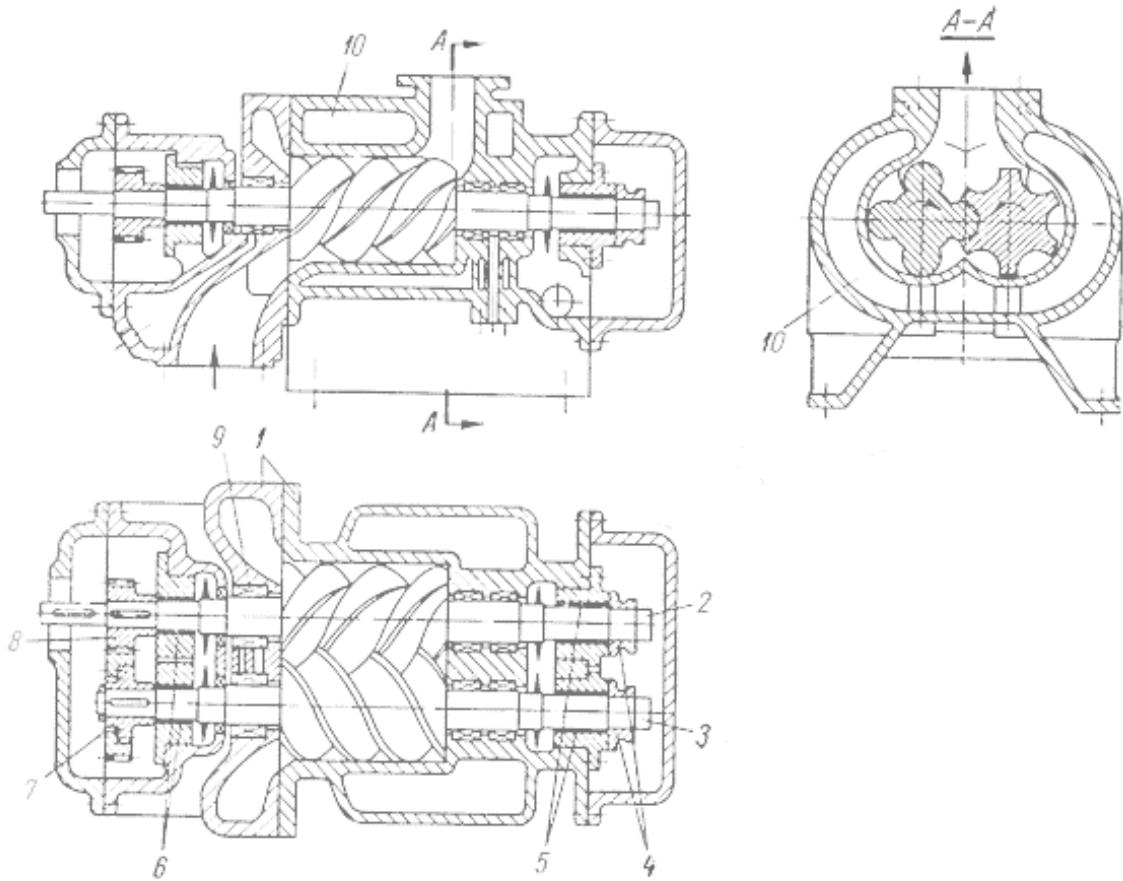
Конструктивна схема гвинтового компресора з охолодженням корпусу
